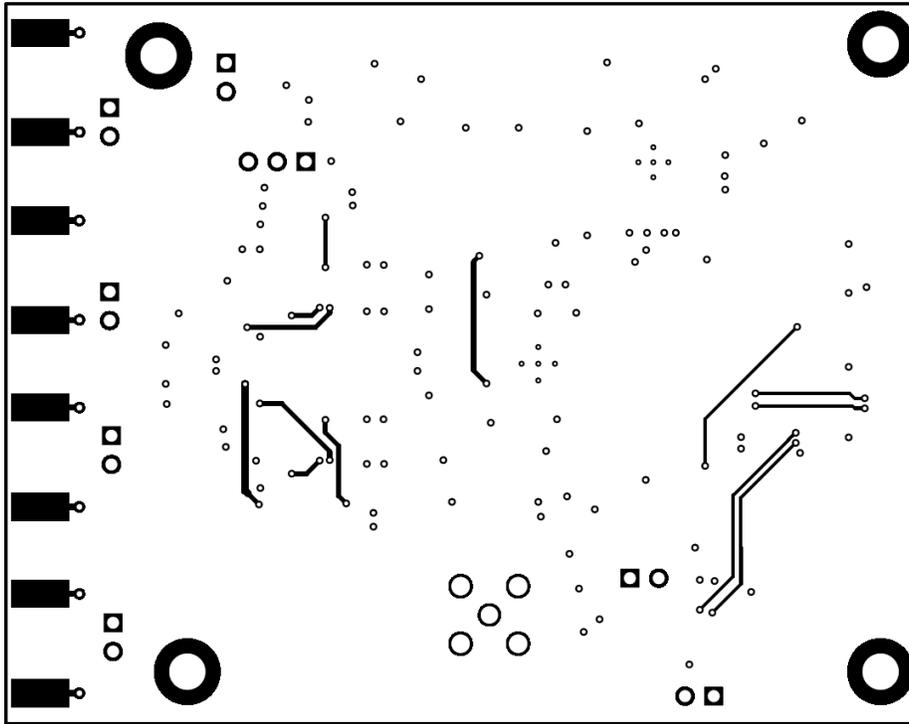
ADS9224REVM PCB レイヤ 4: 下層
